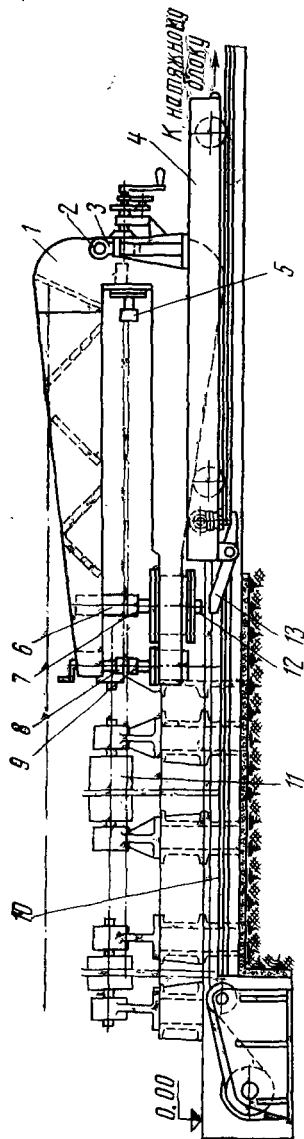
Установка для механизированной сборки кольцевых стыков корпусов цилиндрических сосудов
